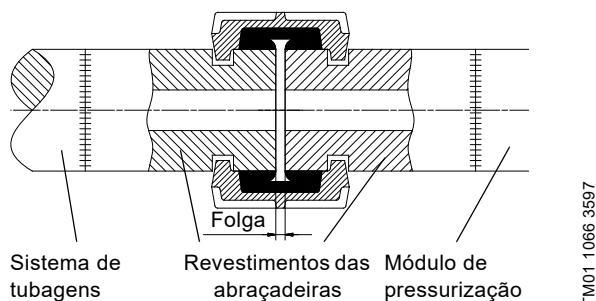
Ligação da tubagem utilizando acoplamentos de abraçadeira
